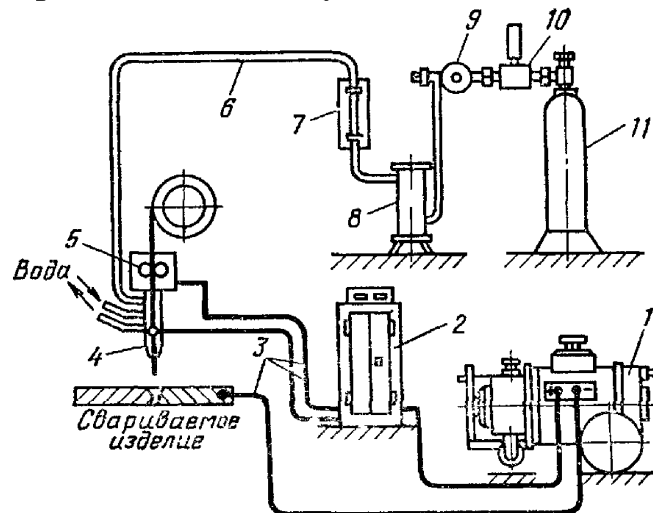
Схема поста для полуавтоматической сварки плавящимся электродом в среде защитного газа
